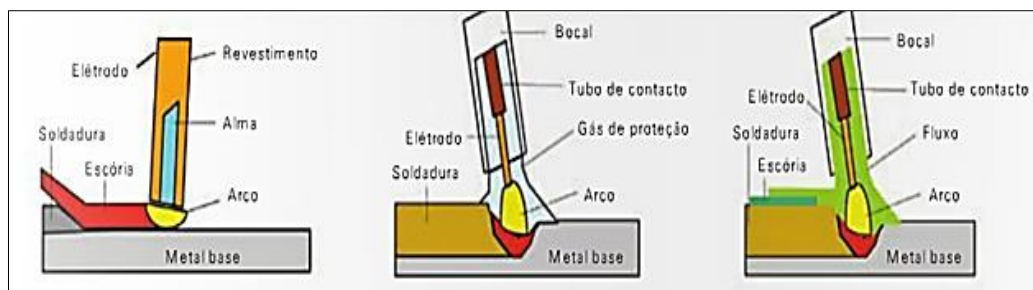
Processos de soldadura: a) Eléctrodo Revestido b) MAG; c) Arco Submerso[53]
